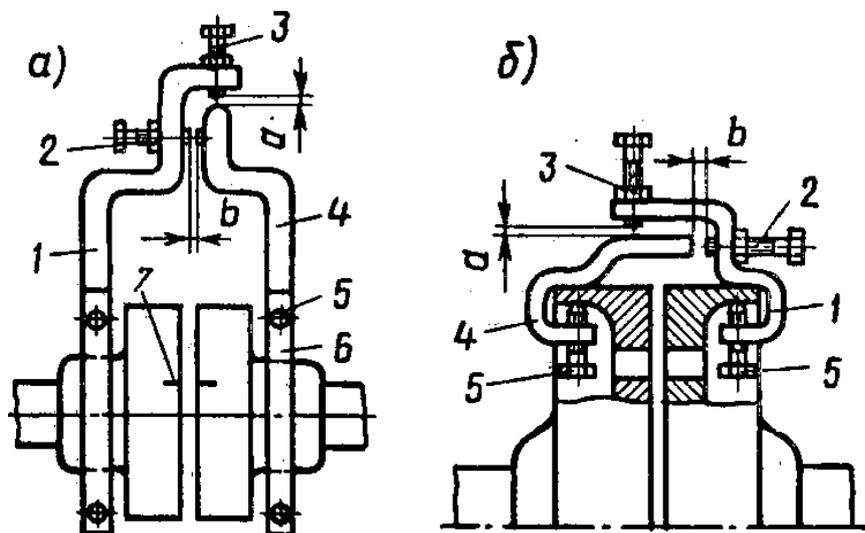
Центровка валов: *а* - центровочные скобы для центровки по втулкам полумуфт; *б* - для центровки по ободам полумуфт; 1,4 - скобы; 2,3 - болты для измерения зазоров; 5 - крепежные болты; 6 - хомут; 7 - риски
